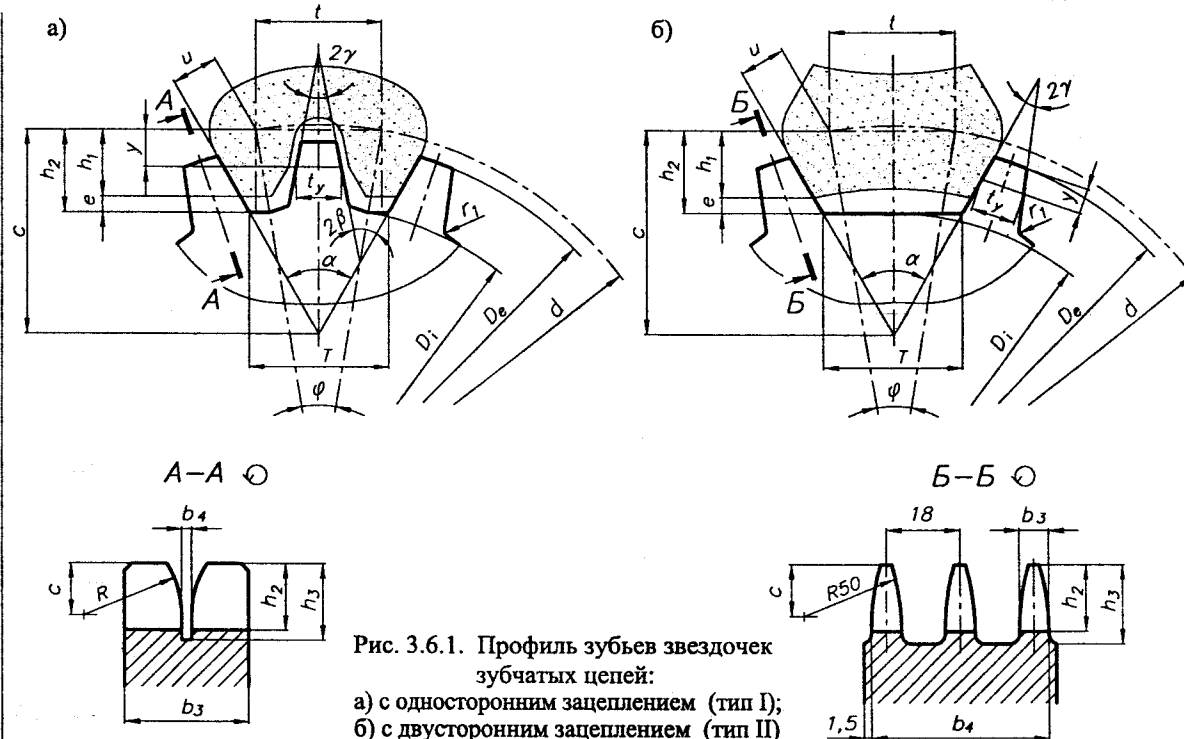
Профиль зубьев звездочек зубчатых цепей:
